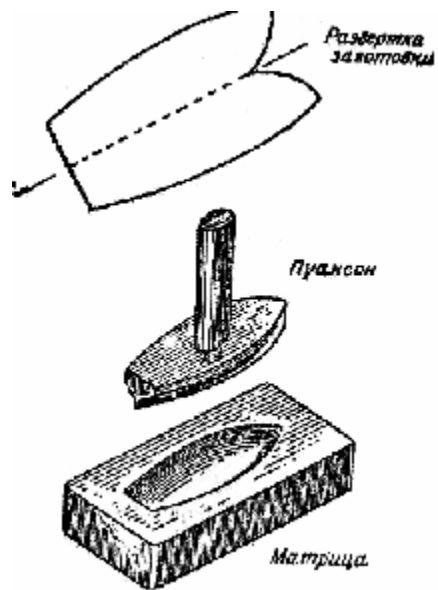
Пресс-форма для штамповки корпуса шлюпки
